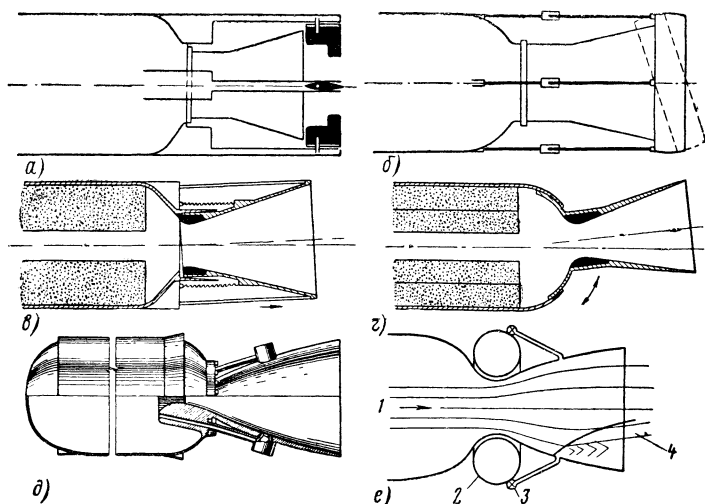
Так можно управлять направлением вектора тяги двигателя твердого топлива (т. е. направлением реактивной струи):
